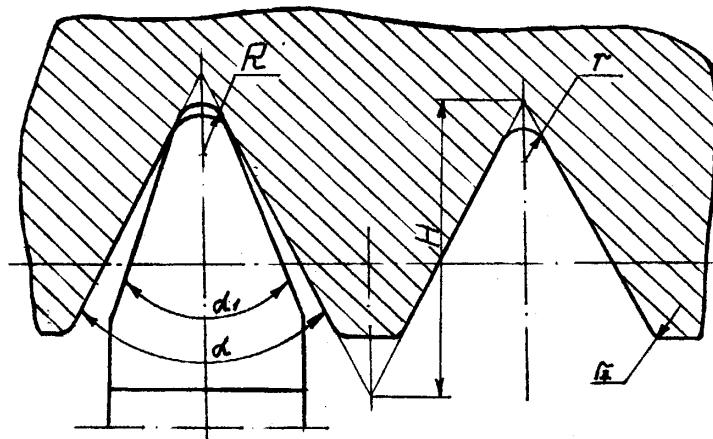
Схема зміцнення різьби робочим інструментом з розрахованими значеннями R і α_1
